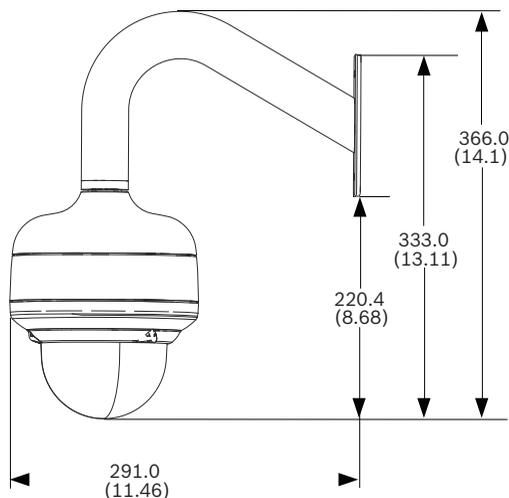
Размеры кронштейна для монтажа на стену
